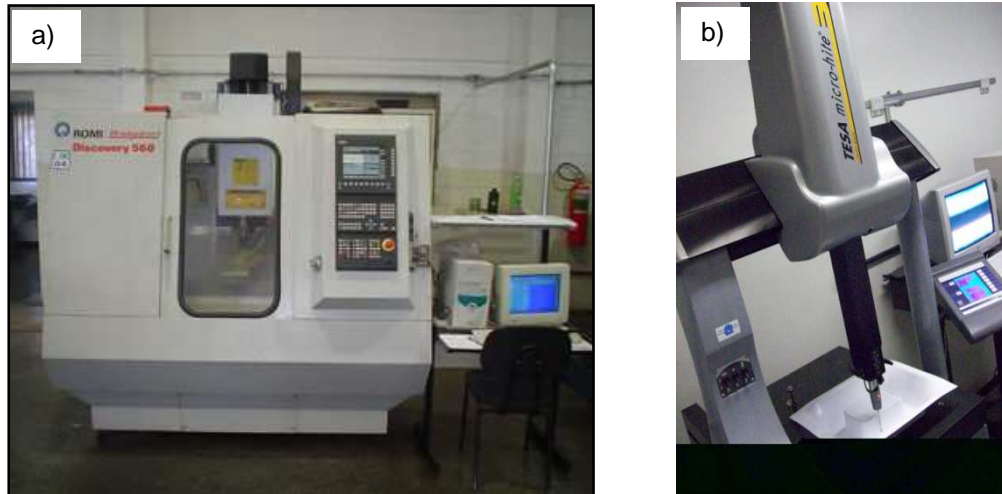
a) Centro de usinagem CNC ROMI *Discovery 560*; b) MMC TESA Micro-Hite 3D.
